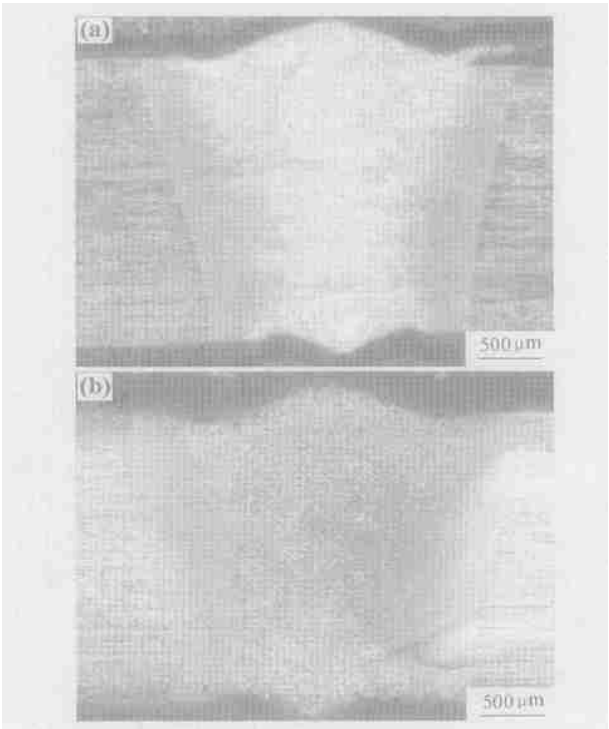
典型焊缝横截面轮廓 (a) 焊接状态; (b) 焊后热处理
